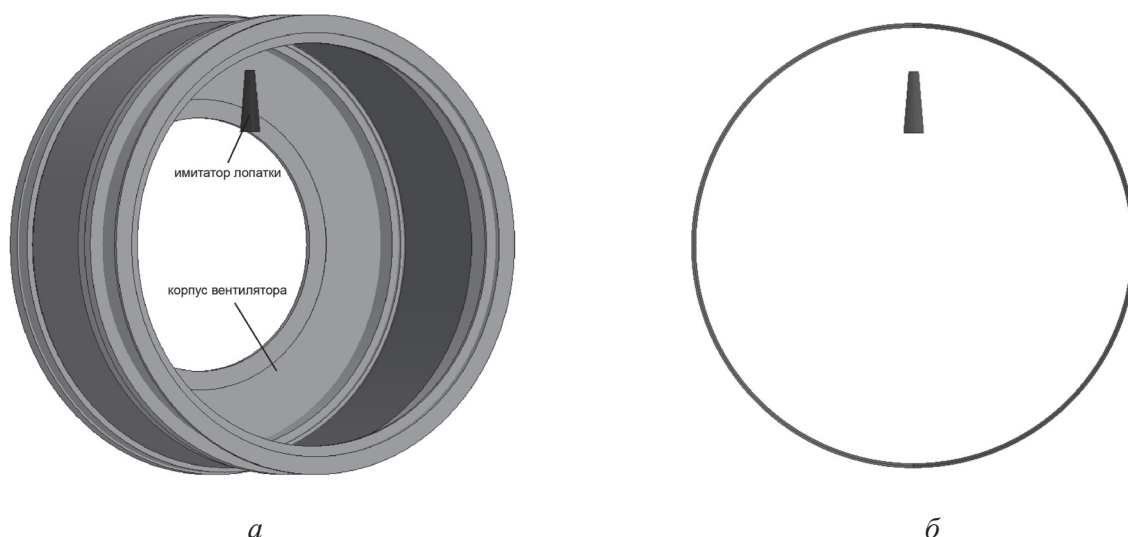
Геометрическая модель (а) и положение имитатора лопатки в момент обрыва (б)
